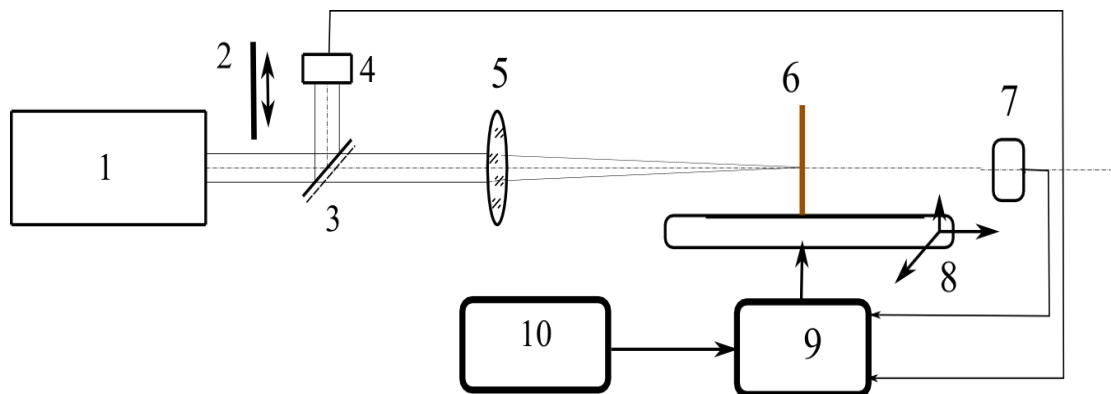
Схема установки для лазерного сверления отверстий. 1 – рабочий лазер, 2 – затвор, 3 – полупрозрачная пластина, 4 – приемник излучения, 5 – линза, 6 – обрабатываемая фольга, 7 – приемник излучения, 8 – трехкоординатный столик, 9 – контроллер, 10 – компьютер.
